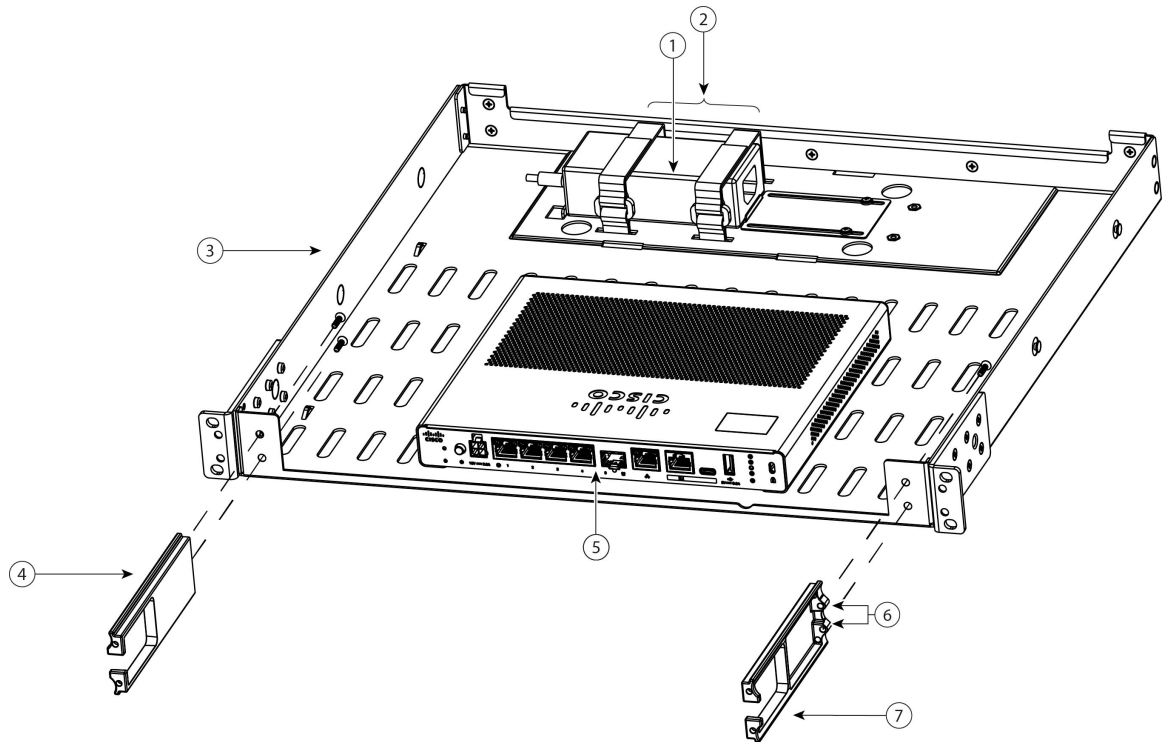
Installazione dello chassis sulla mensola per montaggio in rack
